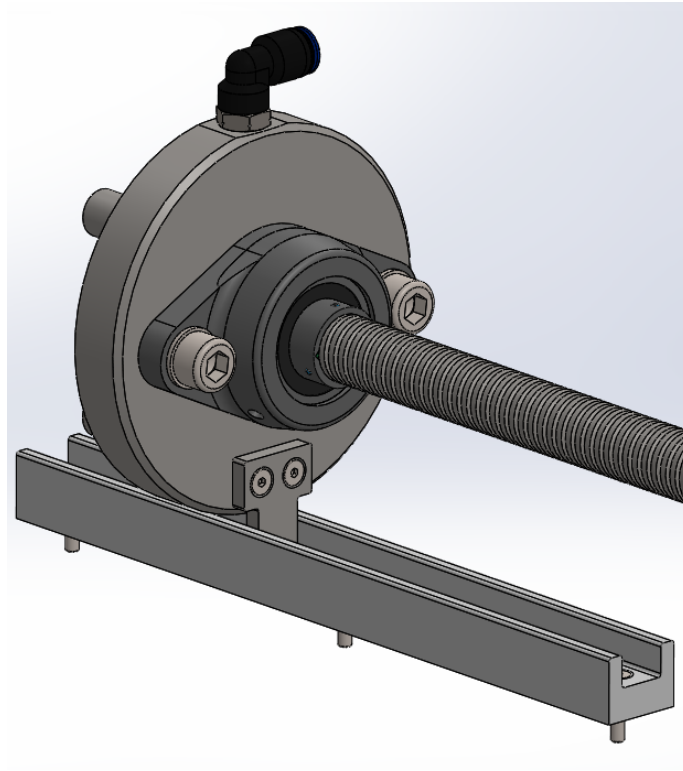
Solução aplicada para apenas conferir movimento linear à flange móvel.
